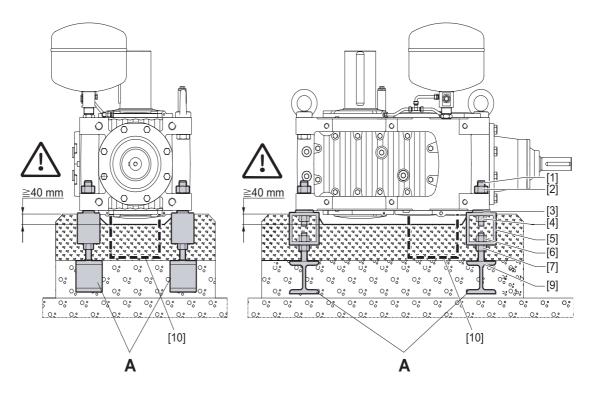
Железобетонный фундамент индустриального редуктора MC.PE.. / MC.RE..
